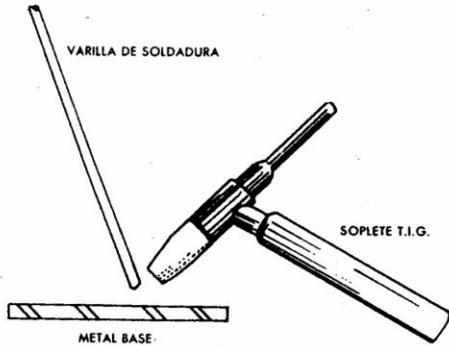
Manera de correr un cordón con varilla de soldadura.
